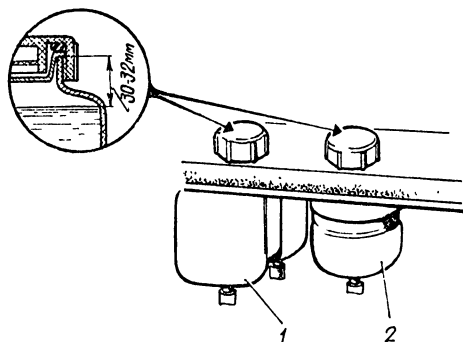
Питательные бачки главного цилиндра тормоза и главного цилиндра выключения сцепления (вид на бачки со стороны багажника):
